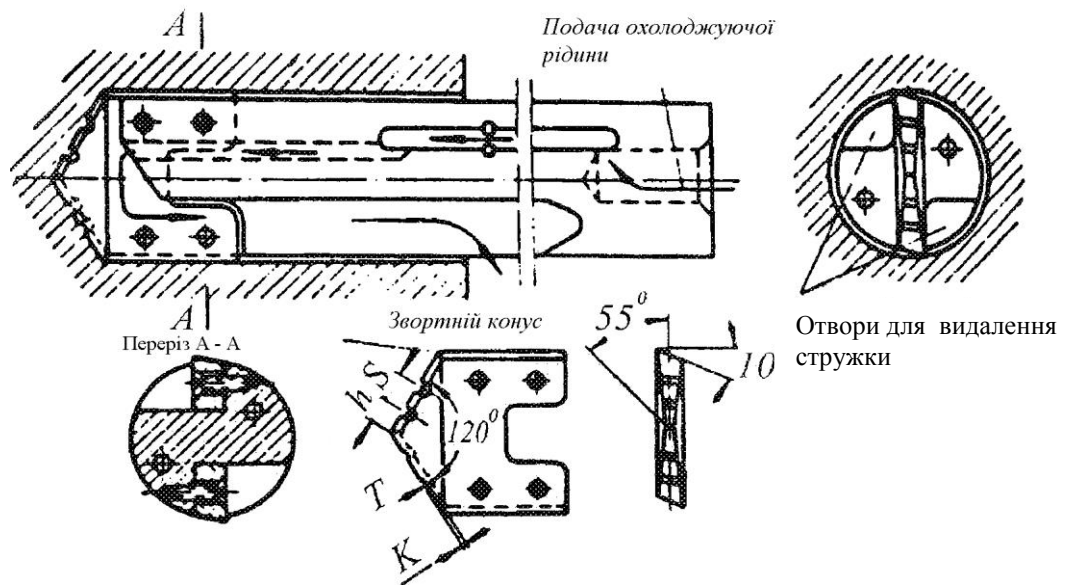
Свердло з двома кромками для глибокого свердління з поліщеними умовами центрування
